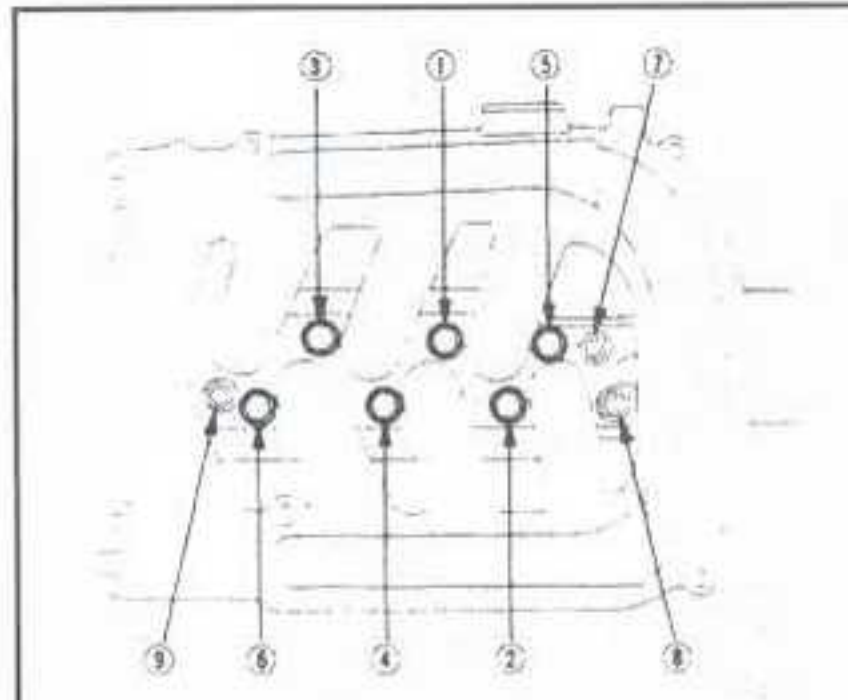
Порядок затяжки болтов впускного коллектора - 3,5 л двигателя V6 моделей Odyssey
